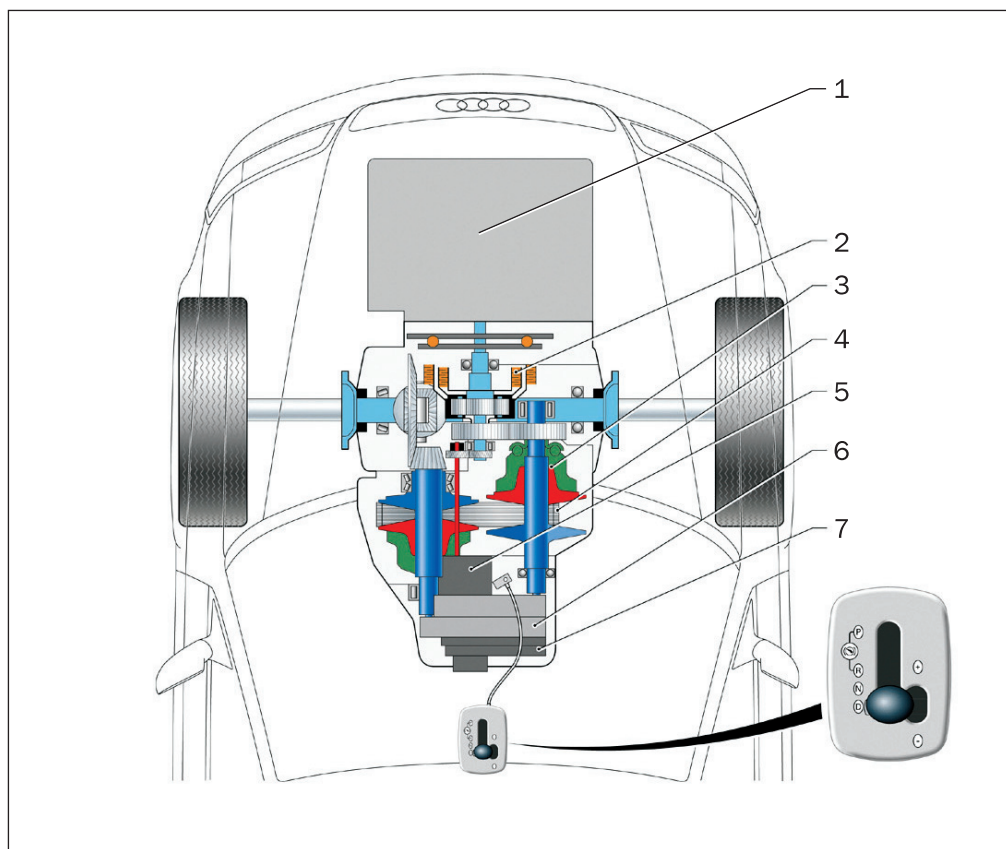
Схема коробки передач Multitronic: 1 — двигатель; 2 — сцепление; 3 — вариатор; 4 — цепь; 5 — гидронасос; 6 — управляющий блок; 7 — блок электроники
